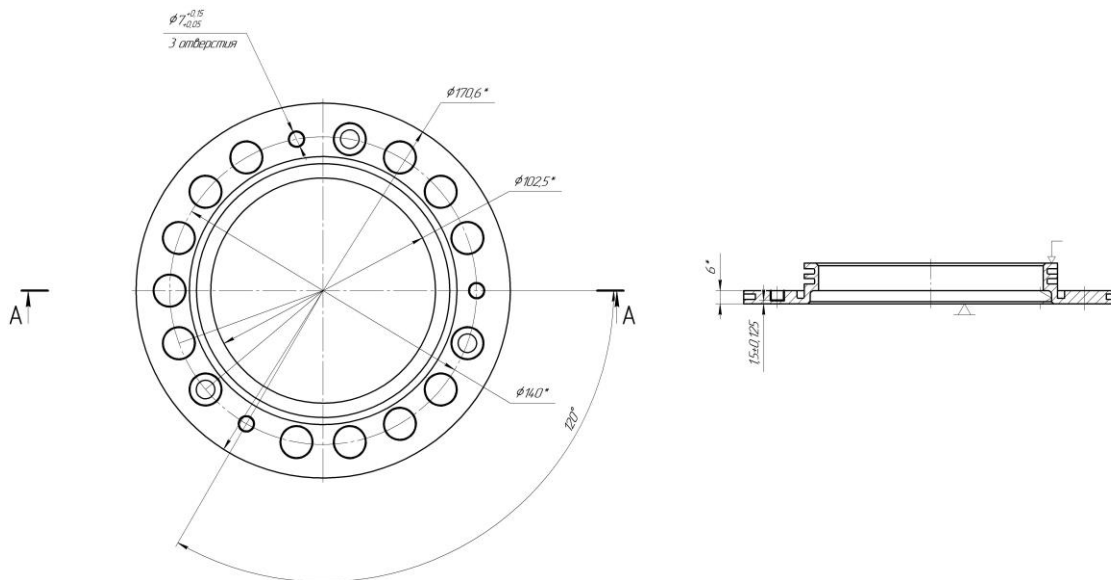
Операційний ескіз на свердлувальну операцію
